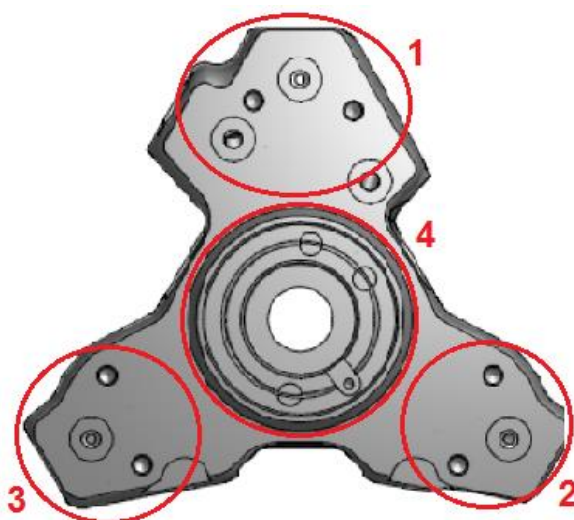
Těleso čerpadla z rodiny 3 [2].
